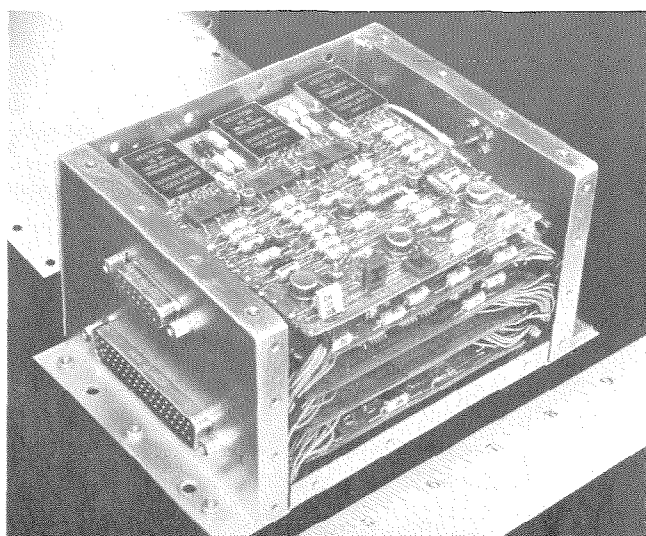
Ensamble típico de tarjetas de circuito impreso.
